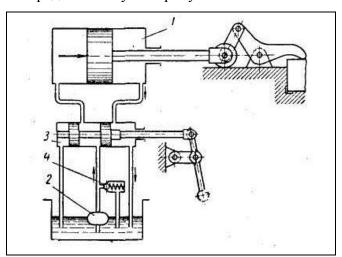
Структурная схема гидропривода станочного приспособления с цилиндром двустороннего действия
